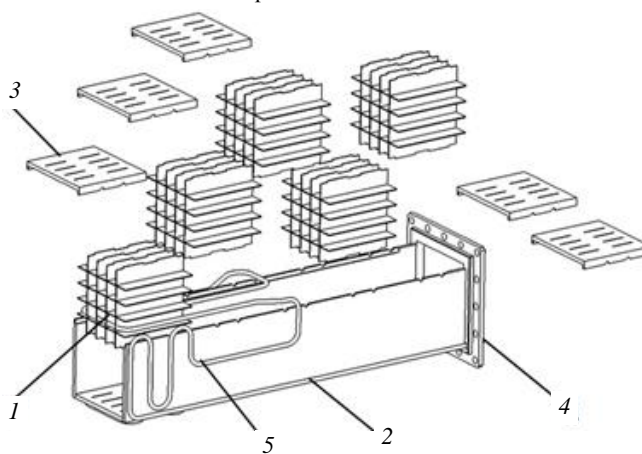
Конструкция вольфрамового коллиматора: 1 — вольфрамовые пластины; 2 — корпус; 3 — крышка; 4 — фланец; 5 — трубка водяного охлаждения
